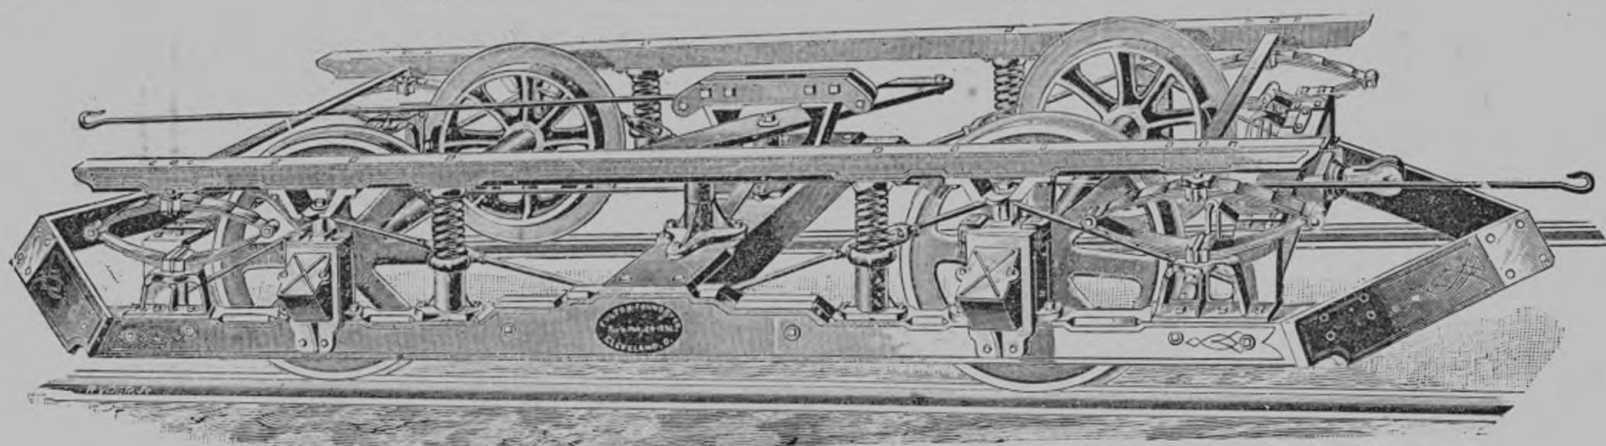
CHASSIS FULTON POUR TRACTION A CABLE
